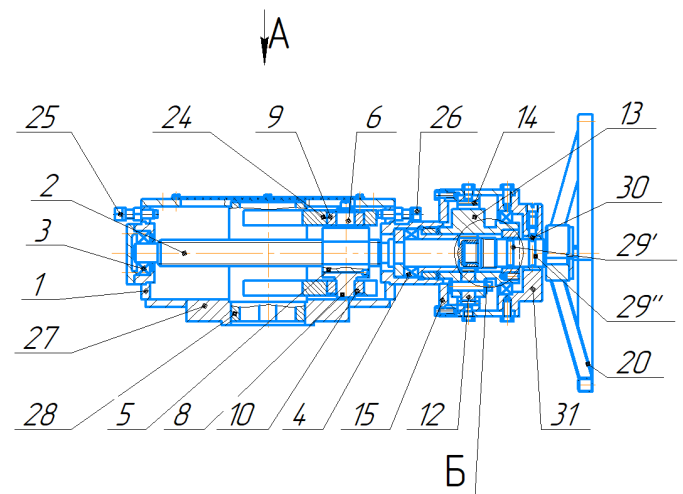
Привод ручной двухскоростной неполноповоротный, патент RU189234U1
